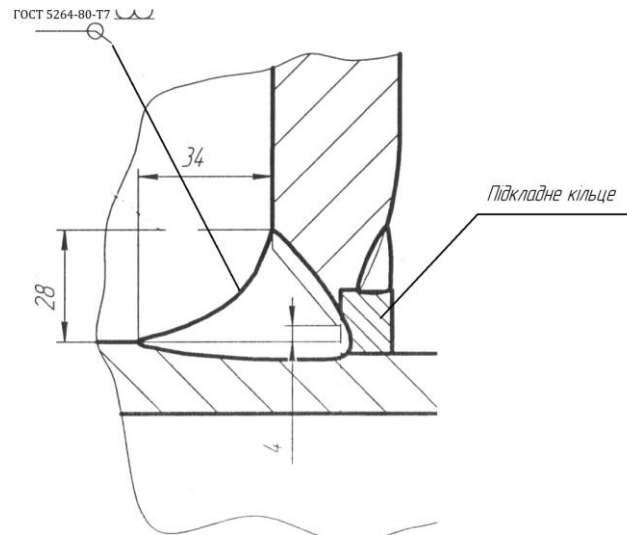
Монтаж та зварювання шва з підкладним кільцем
